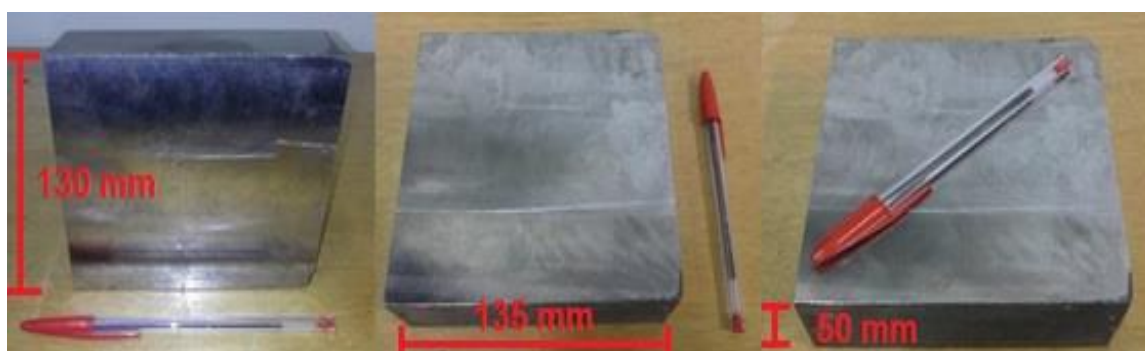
Corpos de prova prontos para os ensaios de usinagem
